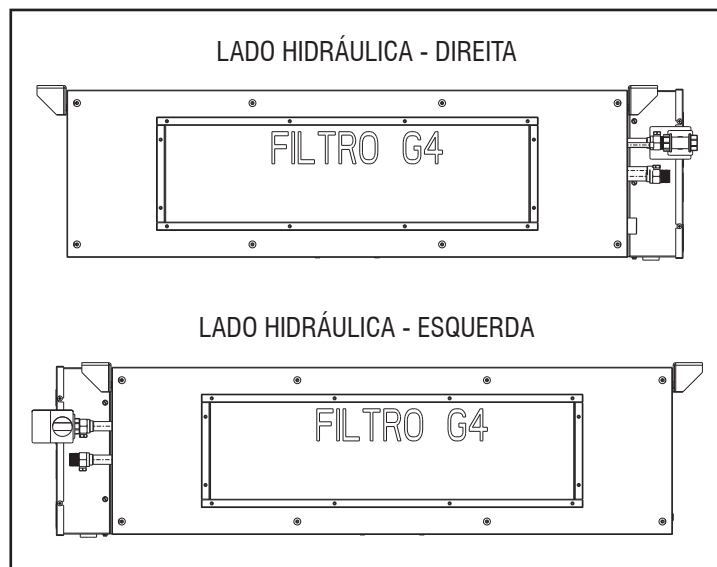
OPÇÕES DE LADO DE MONTAGEM DA HIDRÁULICA
